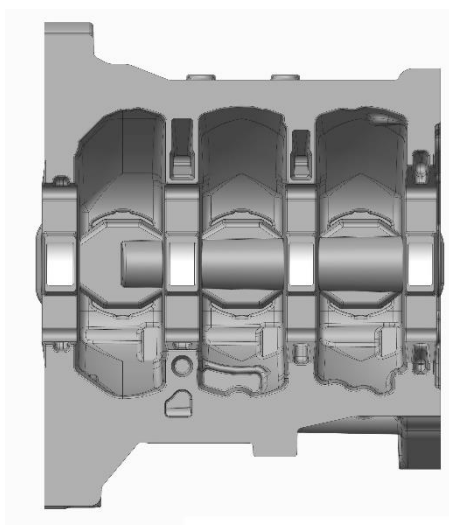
3D model bloku zobrazující horní segment bloku
